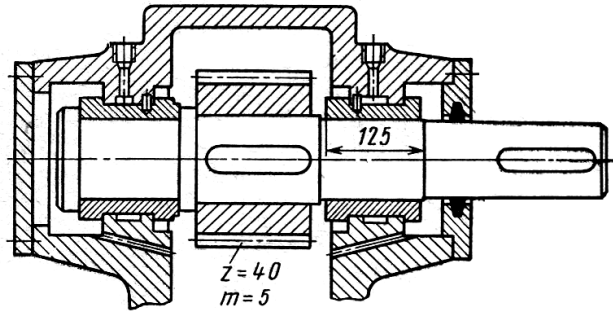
Эскиз вала редуктора с подшипниками скольжения
